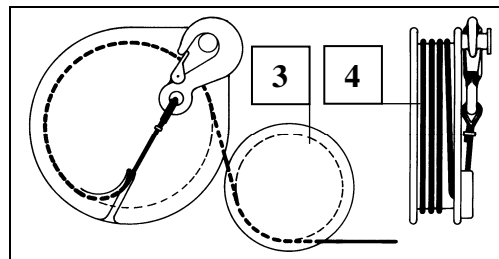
plaqueta em PVC sobre a montagem do cabo
